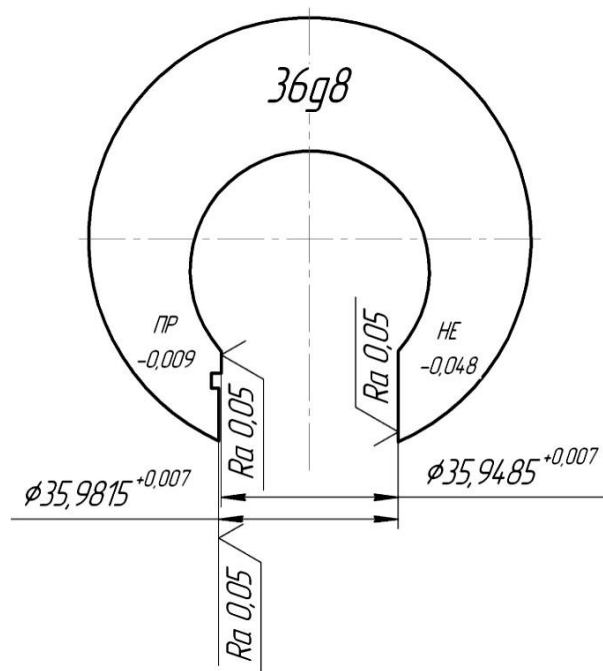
Схема расположения допусков калибров для контроля вала
